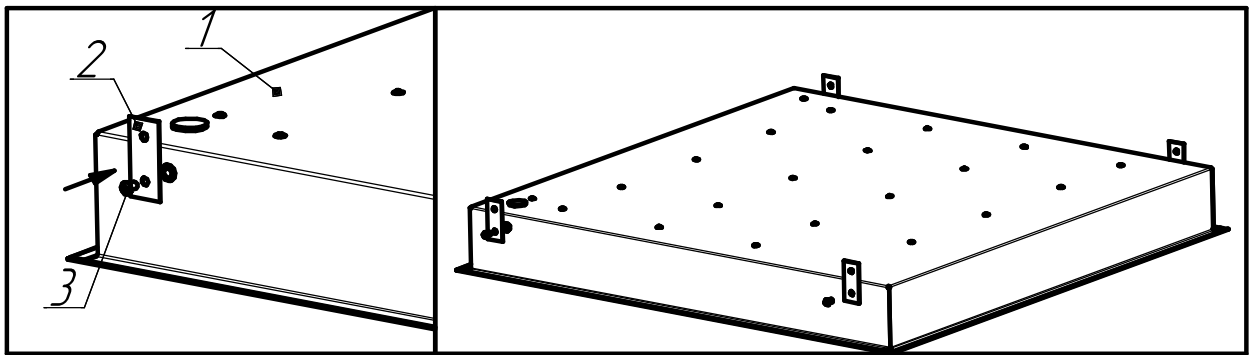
Схема установки пластин для подвеса светильника.
